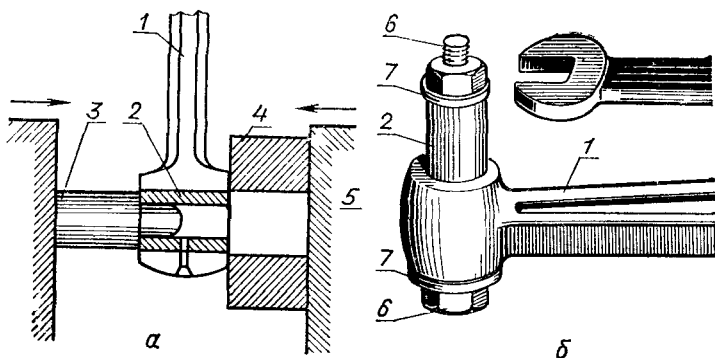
Приспособление для запрессовки и выпрессовки втулки верхней головки шатуна:
